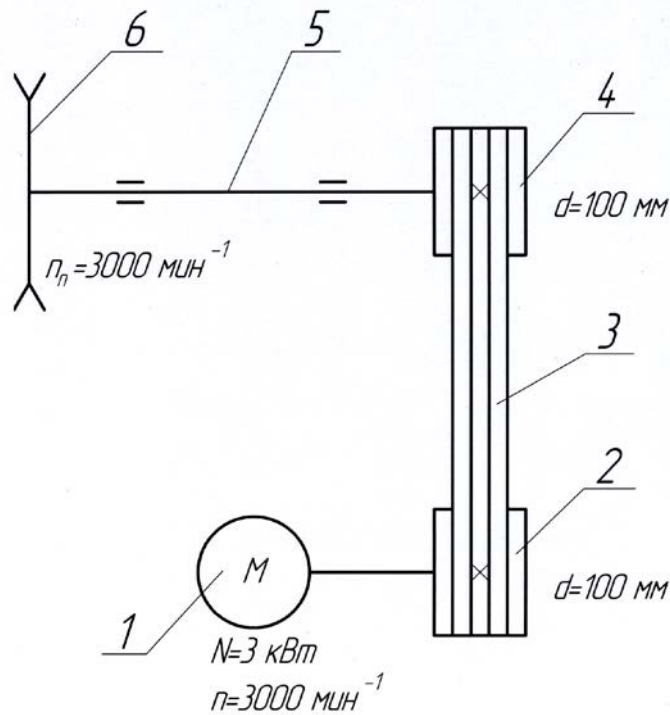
Кінематична схема привода торцювального верстата:
